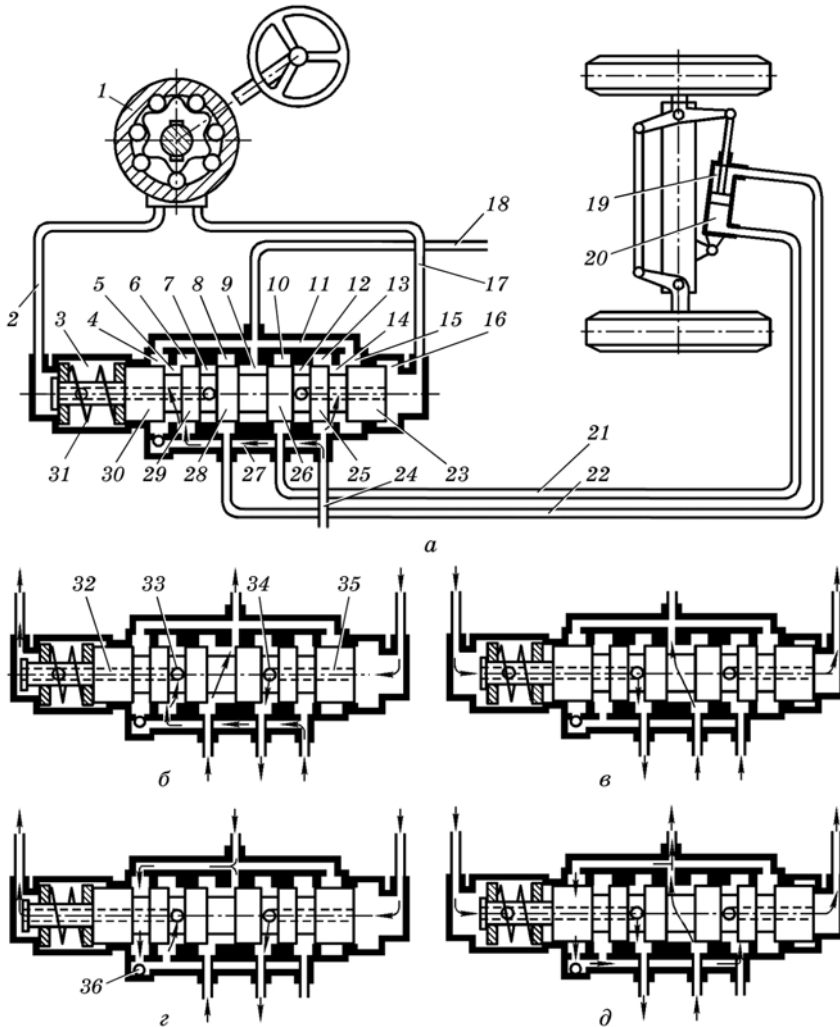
Схема роботи розподільника типу ГА-35000А:
